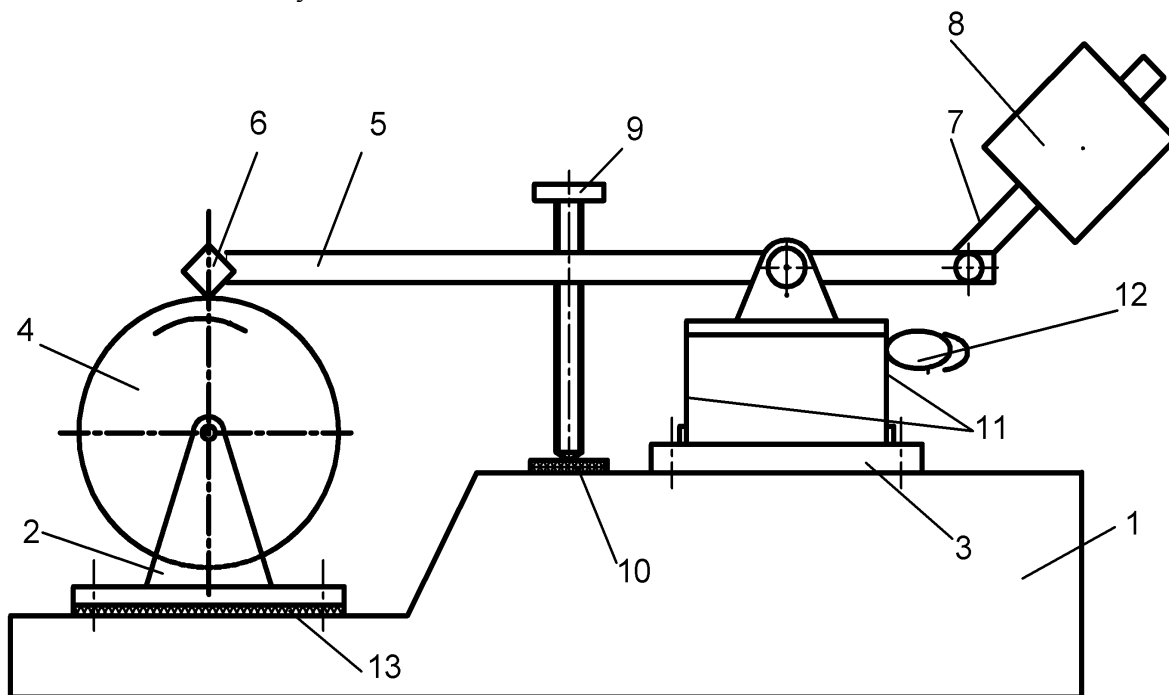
Принципиальная схема модернизированной промышленной распиловочной секции станка модели ШП-2: 1 – основание; 2 – передняя пара стоек; 3 – задняя пара стоек; 4 – распиловочный диск; 5 – стрела; 6 – заготовка; 7 – поворотный рычаг; 8 – противовес; 9 – регулировочный винт; 10 – упругая прокладка; 11 – плоские пружины; 12 – вращающийся кулачок
